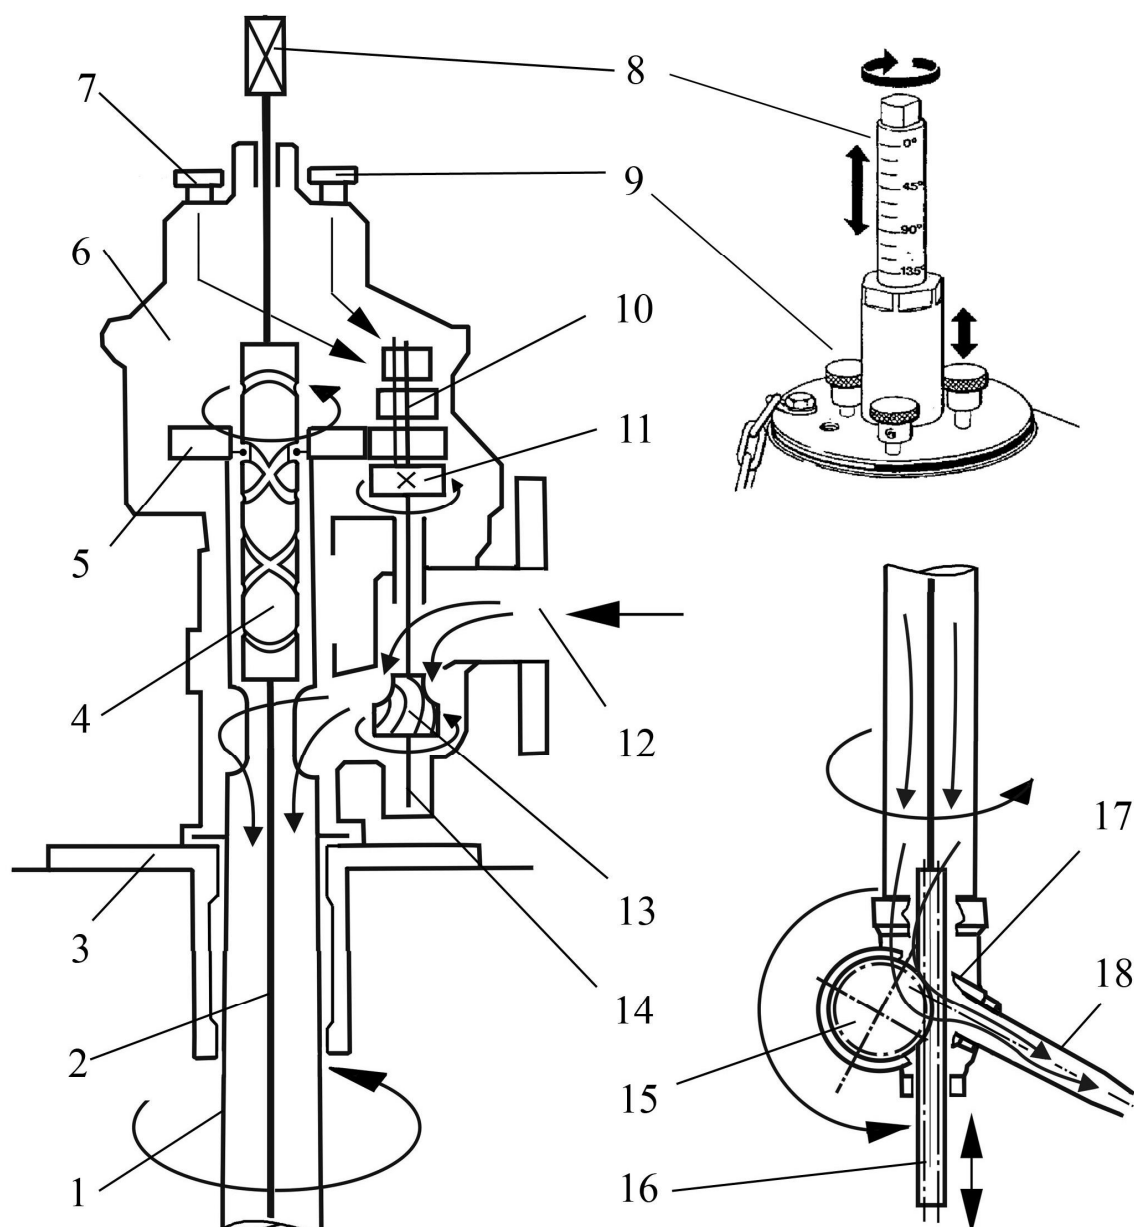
Схема обработки танка одно и двусопловыми ММ
